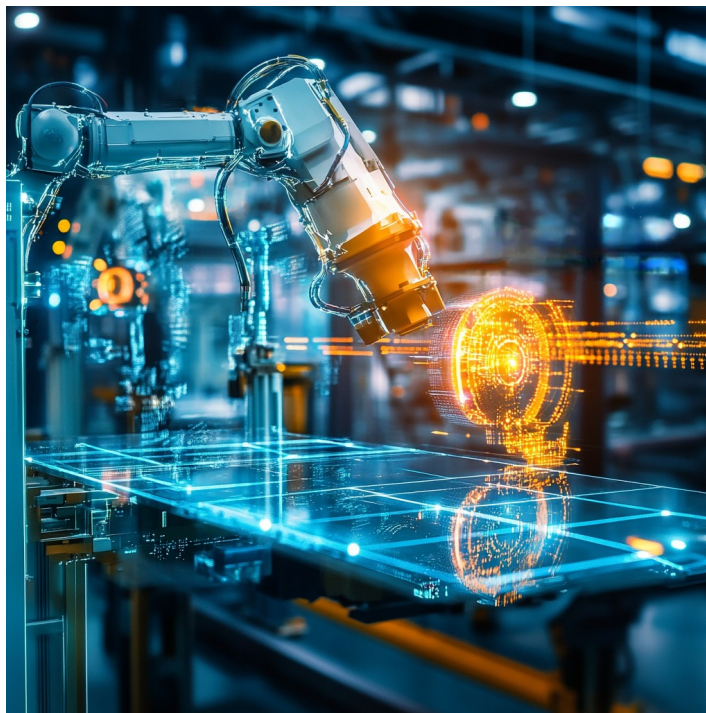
Процес зварювання роботами деталей та обладнання
